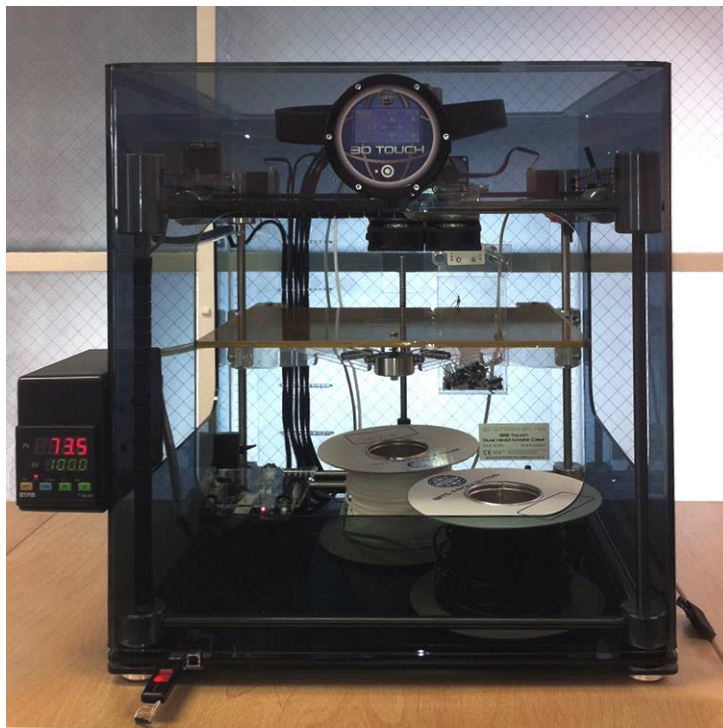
3D Touch [Benchmarking of FDM machines through part quality using IT grades]
